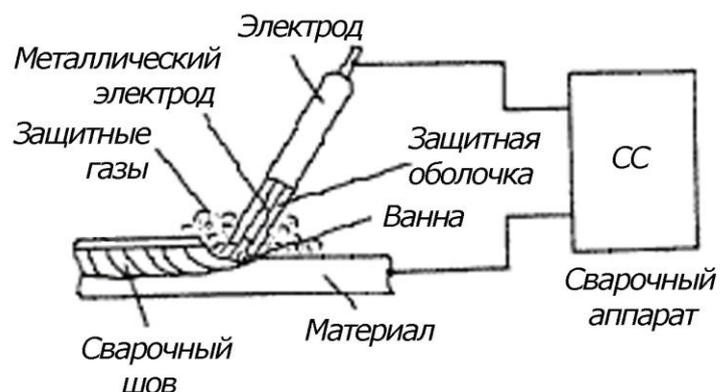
Схема ручной дуговой сварки
